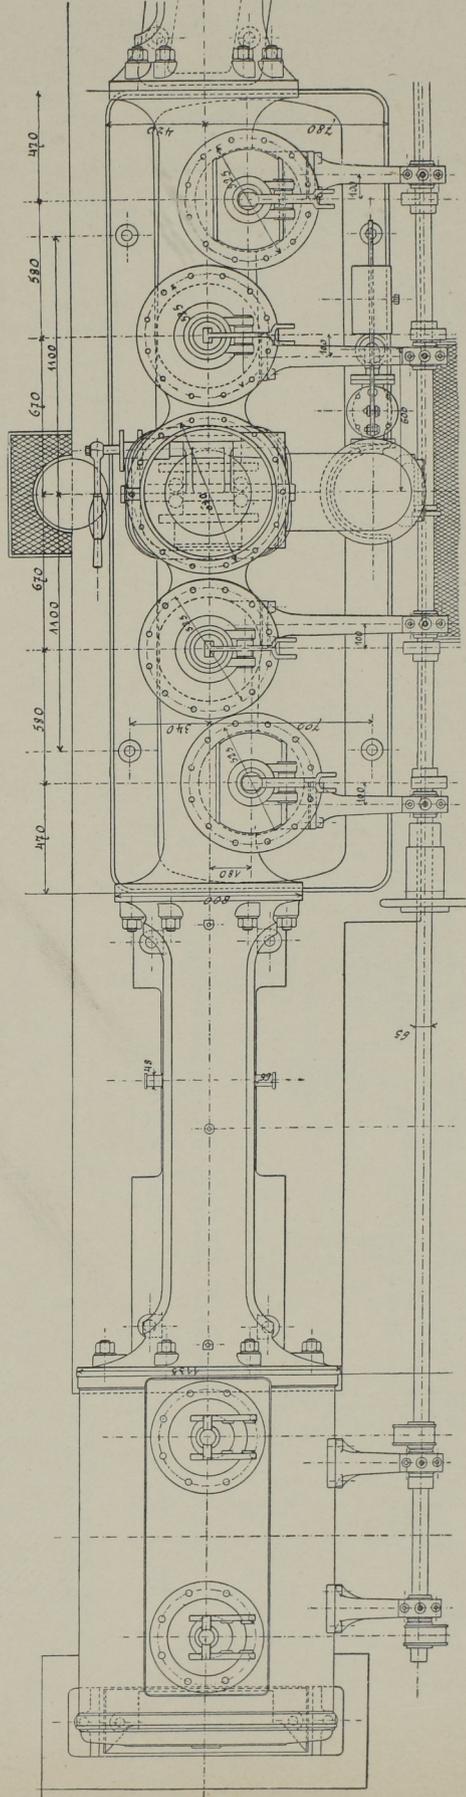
Grundriss der Druckpumpe. Massst. 1 : 30.
